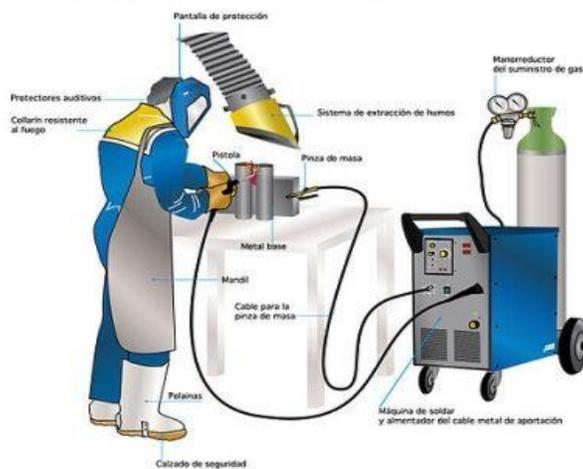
Equipo para soldadura MIG-MAG.
